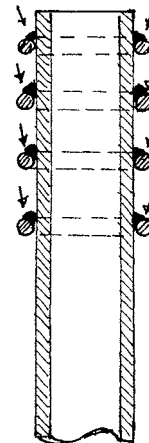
Schéma de cerces soudées sur tube.
